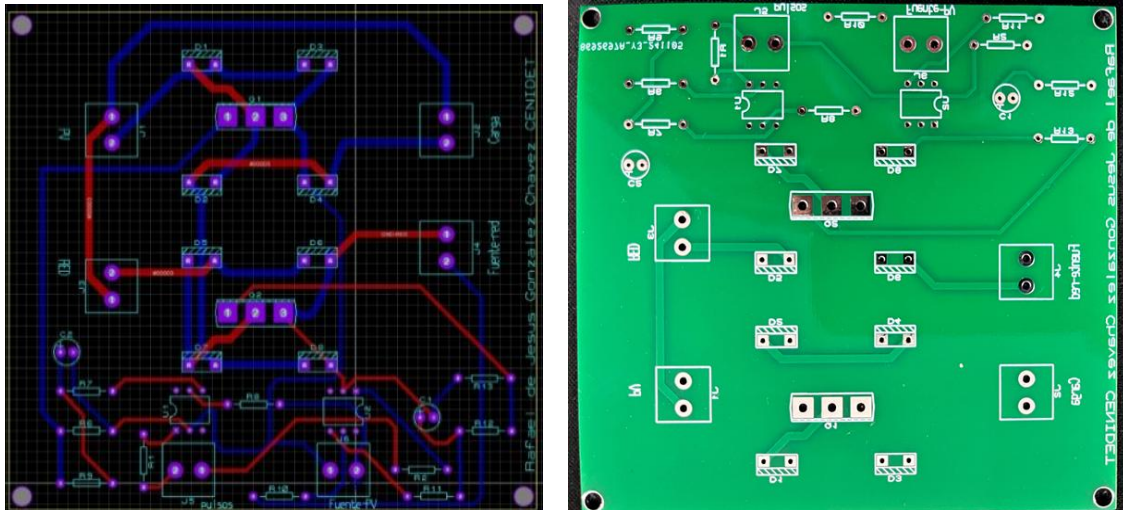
Diseño del PCB (A lado izquierdo) Circuito impreso (B lado derecho).
